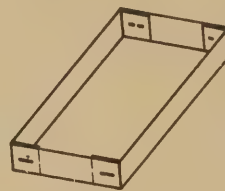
und 5. Schachtel mit Drahtheftung und Einschlageecken.
